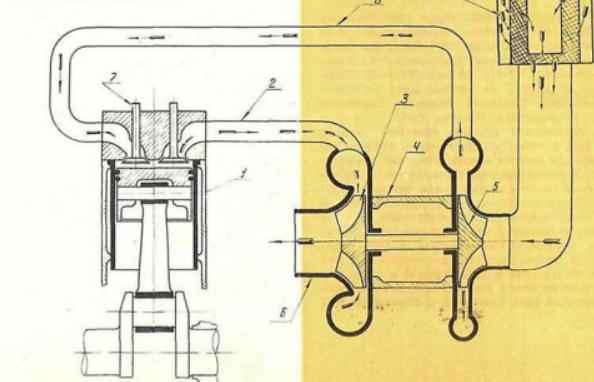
Схемы турбонаддува в одноцилиндровом двигателе: 1 — цилиндр; 2 — выпускной коллектор; 3 — турбина; 4 — корпус приводного нагнетателя; 5 — центробежный компрессор; 6 — выпускная труба; 7 — выпускной клапан; 8 — выпускной трубопровод; 9 — воздухоочиститель.
